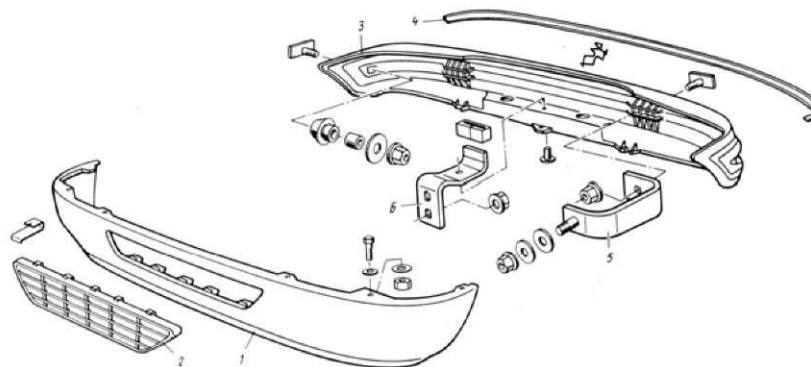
Щитки из композиционных материалов автомобиля: 1 -передний щиток; 2- решетка; 3- задний щиток; 4- декоративная накладка; 5- боковое крепление щитка; 6 - центральное крепление щитка
